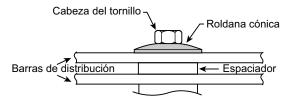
Empalme de las barras horizontales de desplazamiento horizontal
